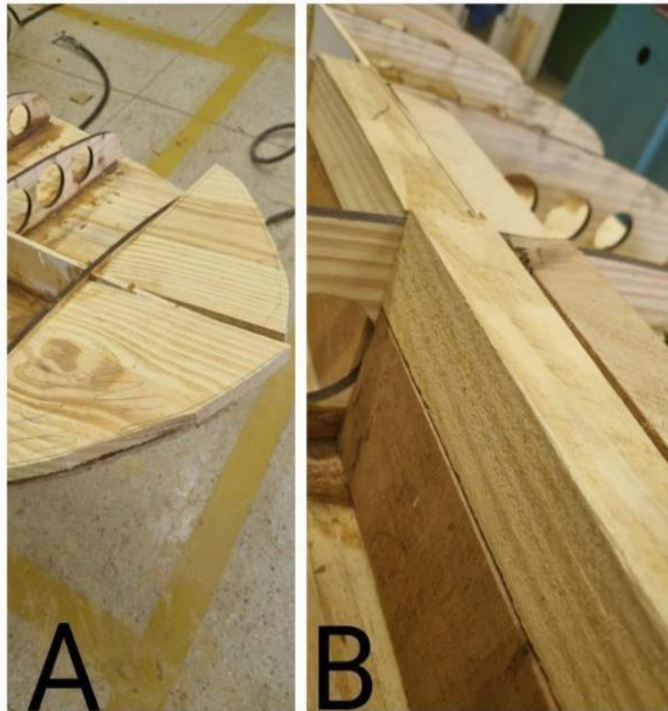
Montagem da estrutura rabeta e colagem do reforço estrutural
